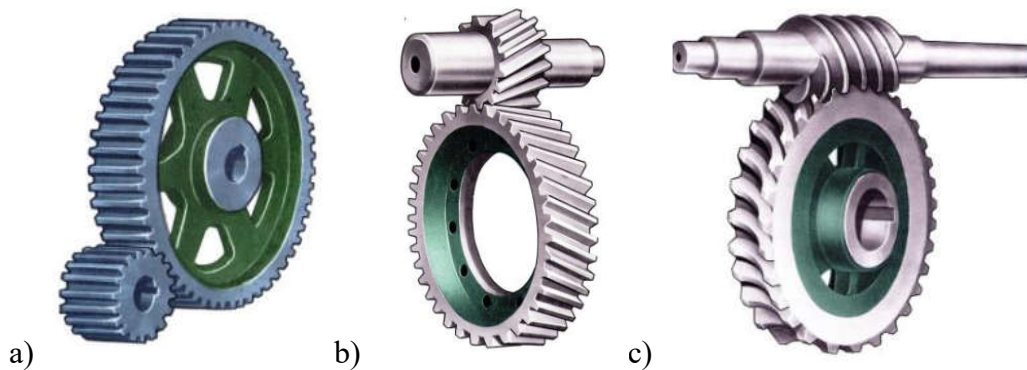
Engrenages externes ; a - engrenage droit ; b - cylindrique hélicoïdal ; c - vis sans fin
